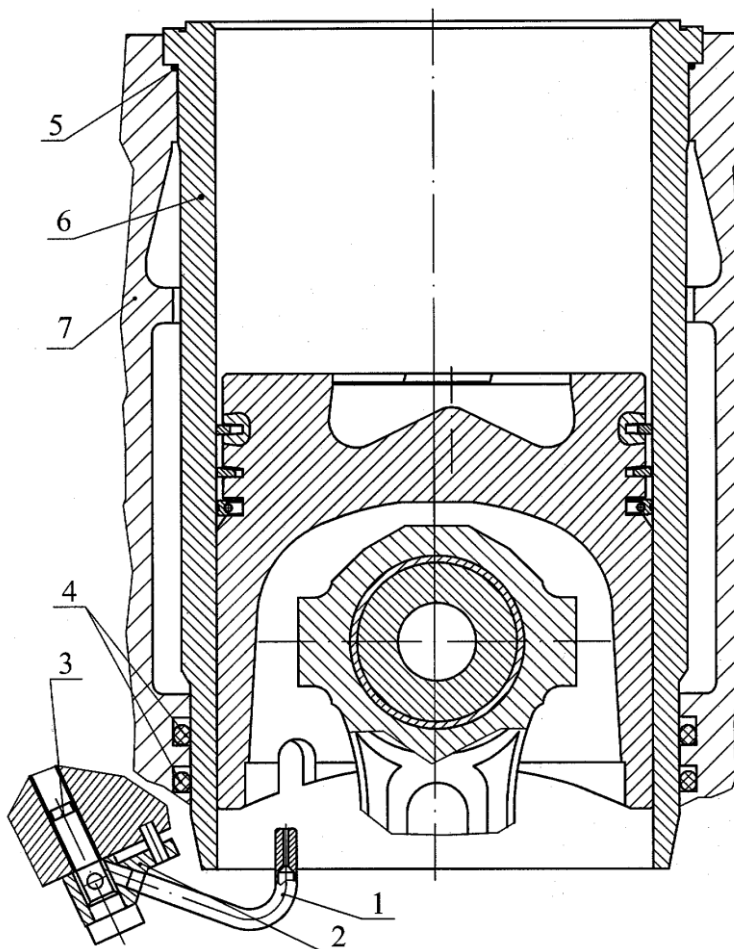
Установка гильзы цилиндра и уплотнительных колец:
